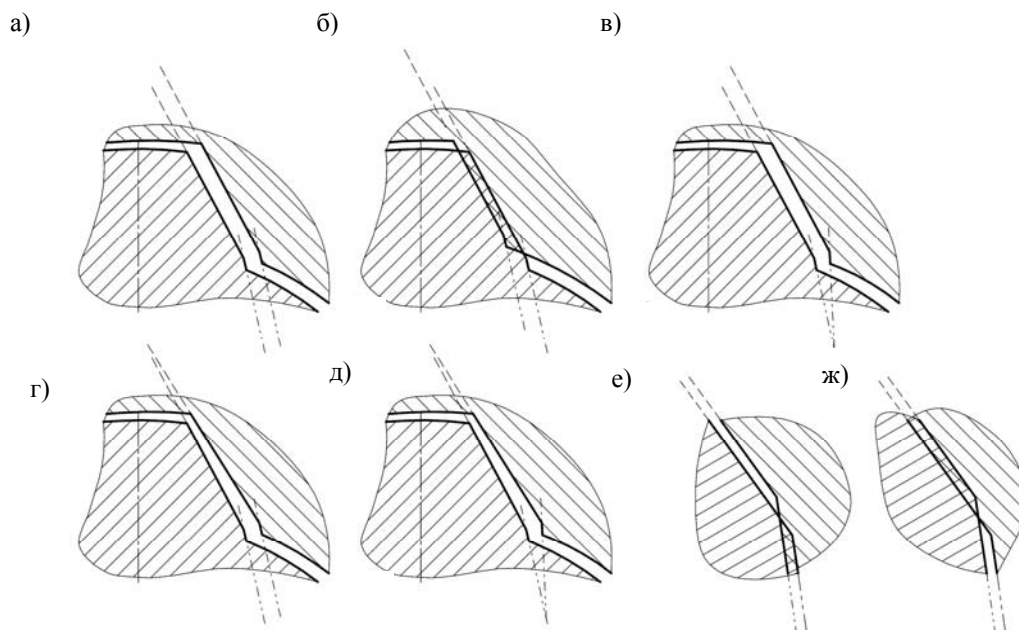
Схемы расположения образующих боковых сторон эвольвентного профиля: а – образующие параллельны с зазором в соединении; б – образующие параллельны с натягом в соединении; в, г – одни образующие параллельны, другие образующие пересекаются с зазором (натягом) в соединении; д – образующие пересекаются с зазором (натягом) в соединении; е, ж – образующие параллельны с зазором и натягом в соединении
